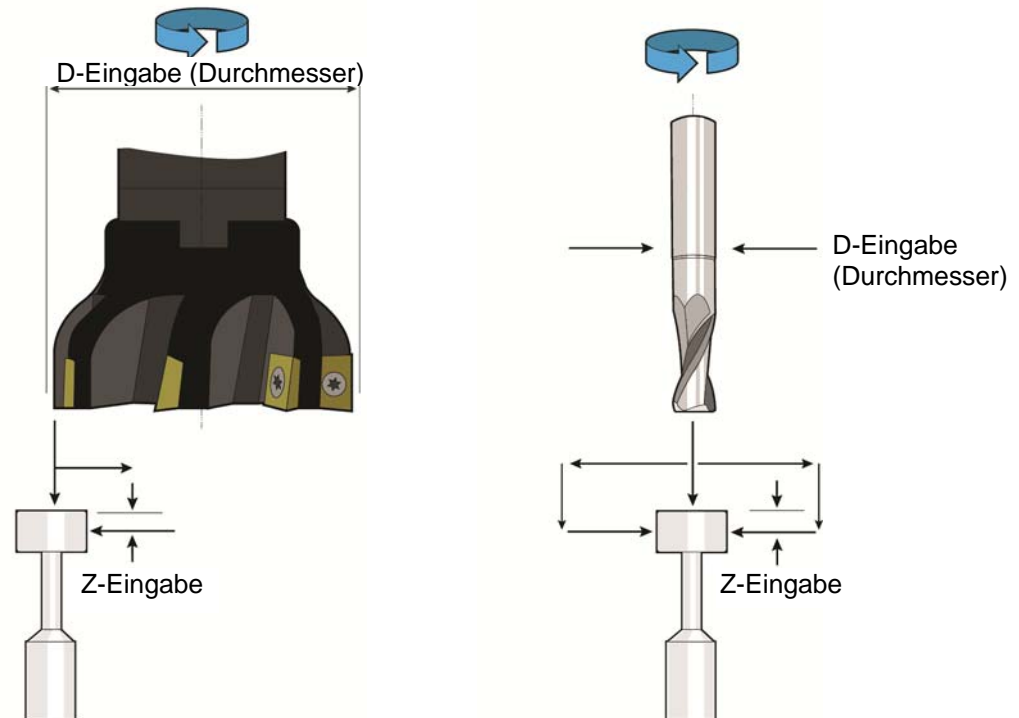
Messung des Radius eines rotierenden Werkzeugs
